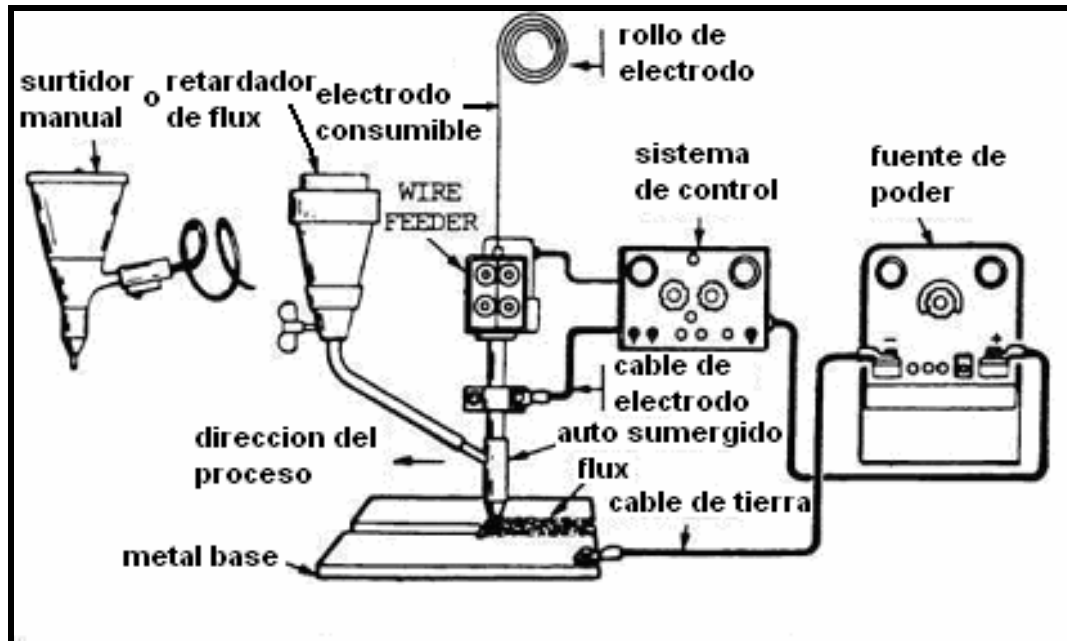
Componentes de un cabezal de soldadura en el proceso de arco sumergido.
